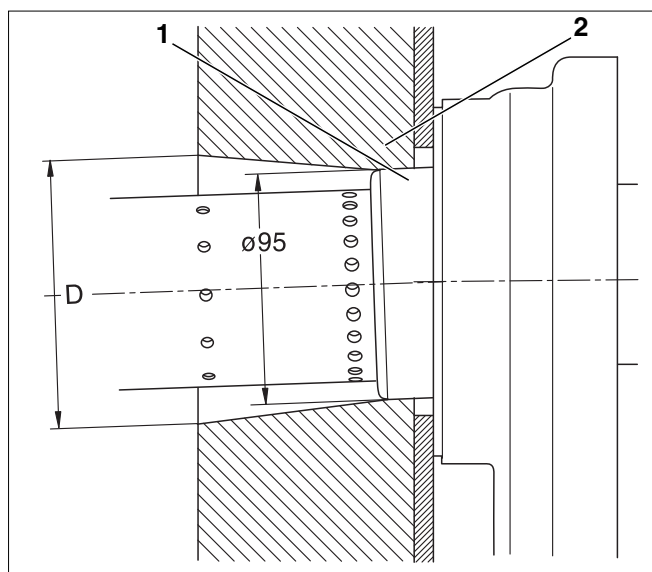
Esquema de corte de la sección de la puerta (medida en mm)
